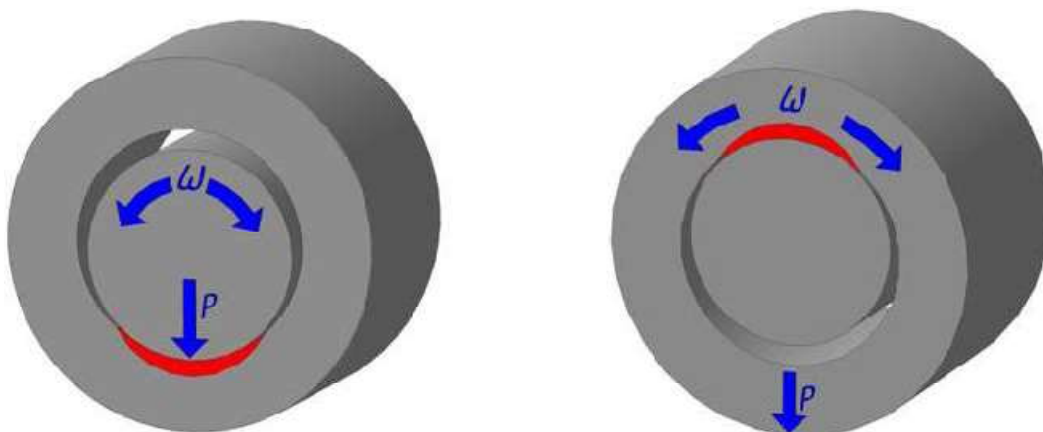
Схеми контактної взаємодії деталей гладких циліндричних рухомих з'єднань: а - опорний отвір та рухомий вал; б - опорний вал і деталь з отвором, що спирається на вал
